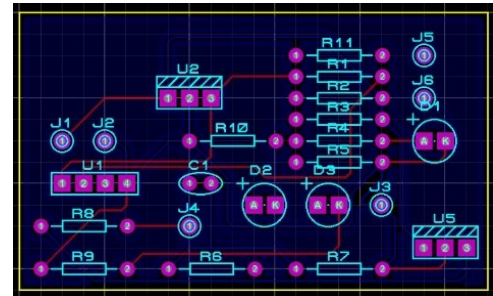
Esquema de la PCB del circuito general Fuente: Propia
